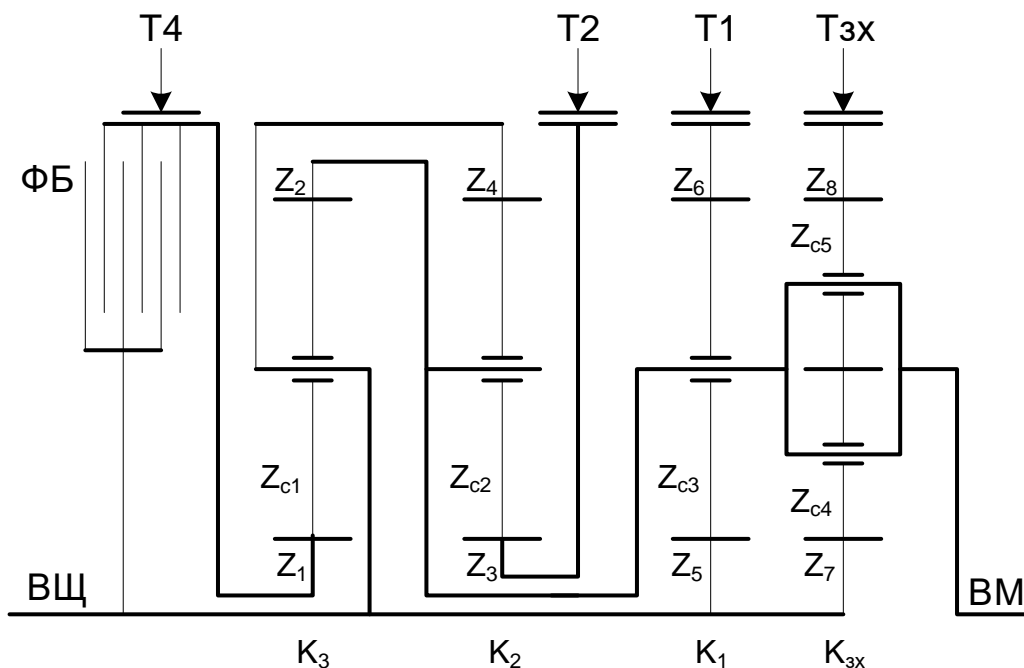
Кинематическая схема планетарной коробки передач типа 4+1 с двумя степенями свободы
